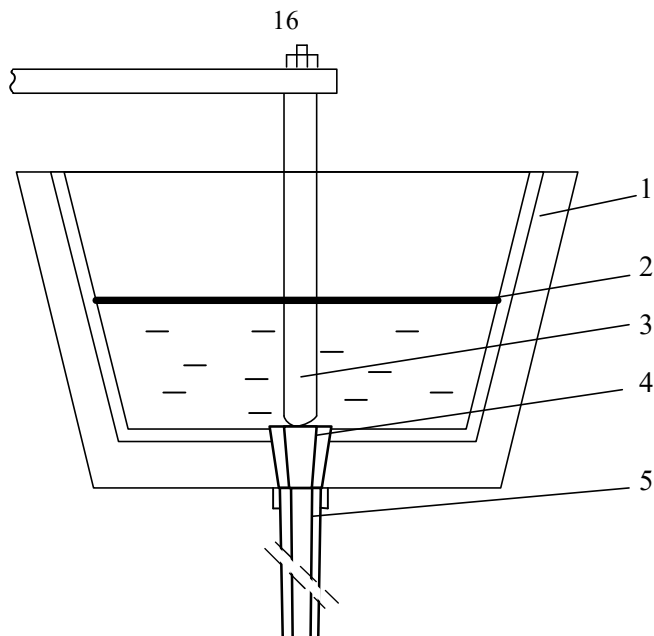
Общий вид промежуточного ковша: 1 - рабочий слой стенок ковша; 2 – уровень жидкого металла; 3 – стопор-моноблок; 4 – стакан-дозатор; 5 – погружной стакан.
